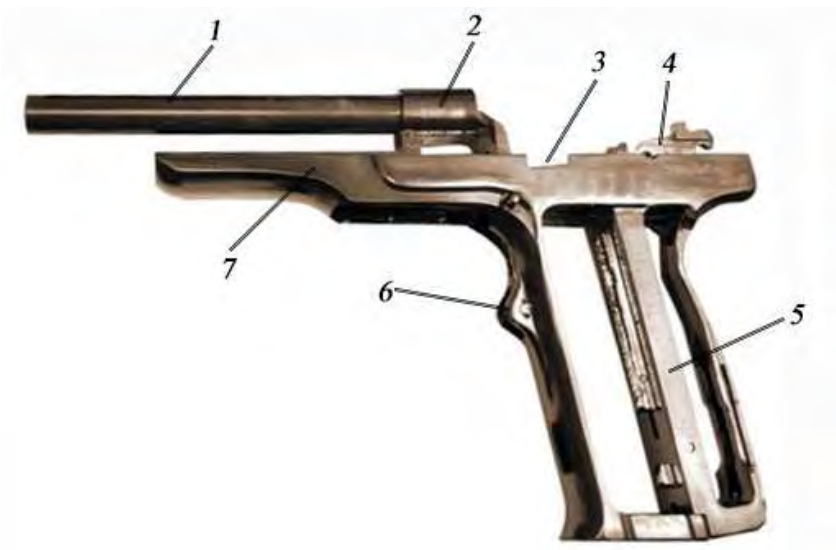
Рамка со стволом и рукояткой: 1 – ствол; 2 – стойка; 3 – вырез для затворной задержки; 4 – выступ с цапфенными гнездами; 5 – перемычка; 6 – прилив; 7 – рамка
